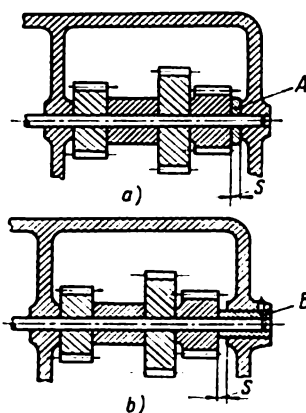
Schéma d'assemblage suivant le procédé de réglage:
